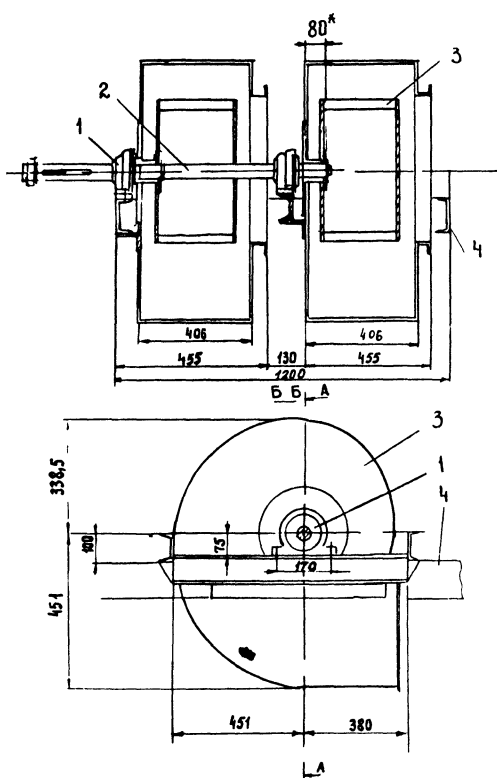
Вентиляційна установка: 1 – підшипникові опори; 2 – вал приводу вентилятора; 3 – вентилятори Ц13-36 № 5; 3 – рама
